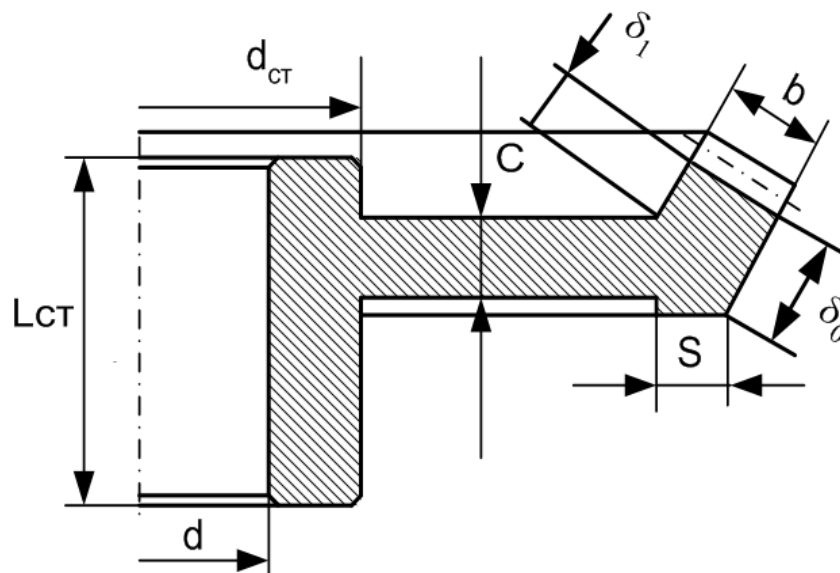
Половина конического зубчатого колеса в разрезе
